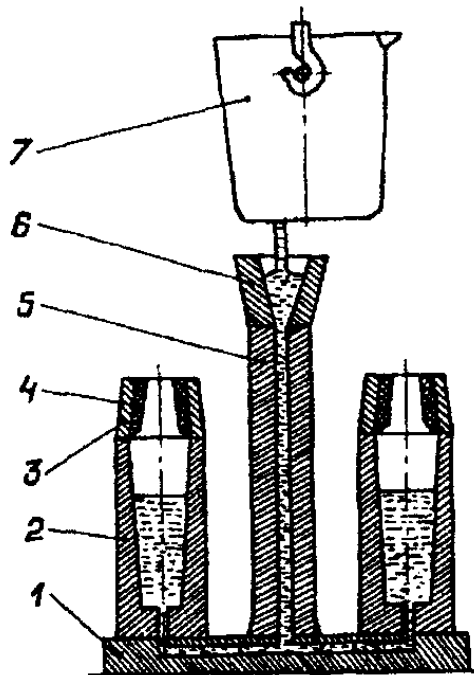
Сифонне розливання сталі [2]: 1 - піддон; 2 - виливниця; 3 - присторова надставка; 4 — футеровка надставки; 5 - центровий ливник; 6 — чаша; 7 — ківш для розливання сталі
